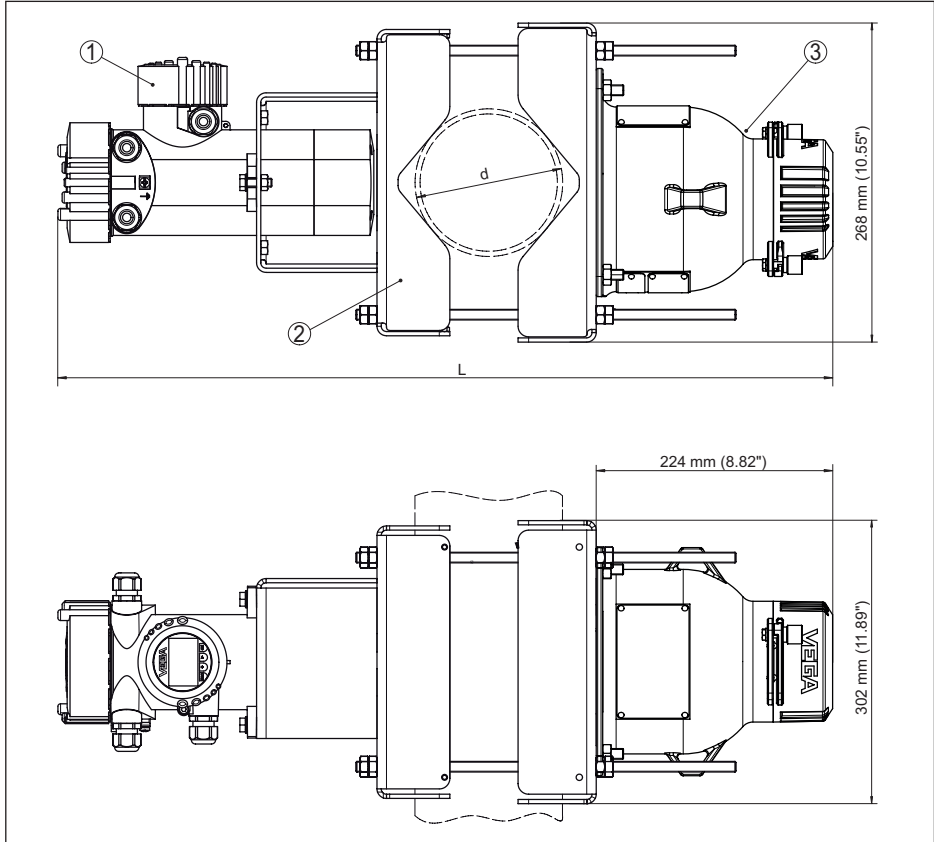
Dispositivo de sujeción con sensor montado horizontalmente (con VEGASOURCE 81, 82, 83)
